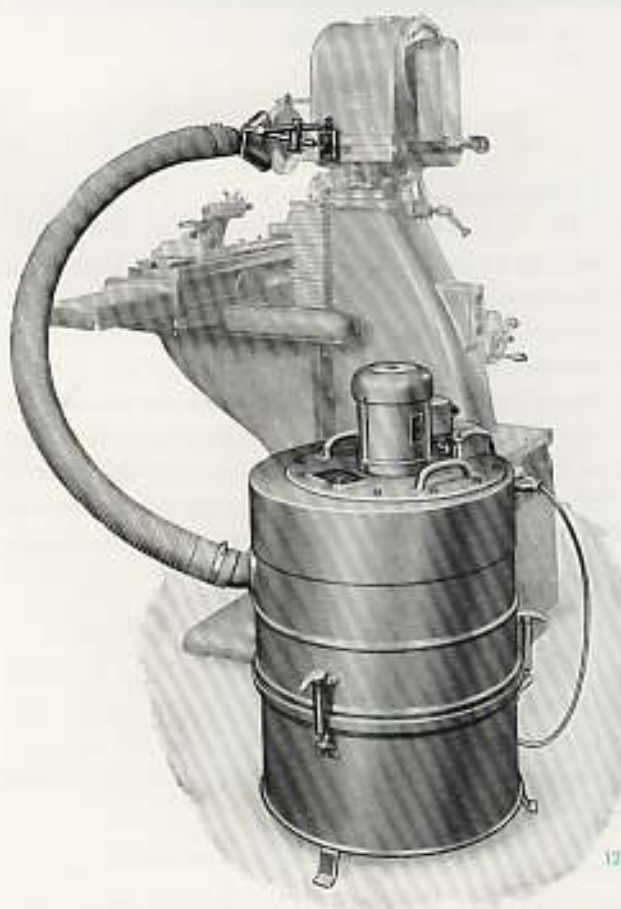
, Schleifstaubsauger Nr. 0.56 an einer SCHÜTTE Werkzeugschleifmaschine WU 3 m5
